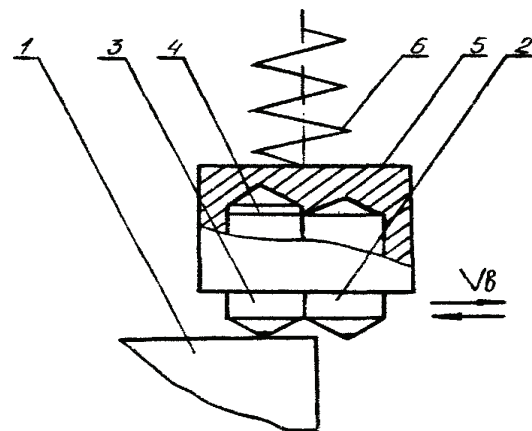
Схема выглаживания двухинденторным инструментом: 1 – деталь; 2,3 – выглаживающие наконечники; 4 – прокладка; 5 – держатель; 6 – пружина
